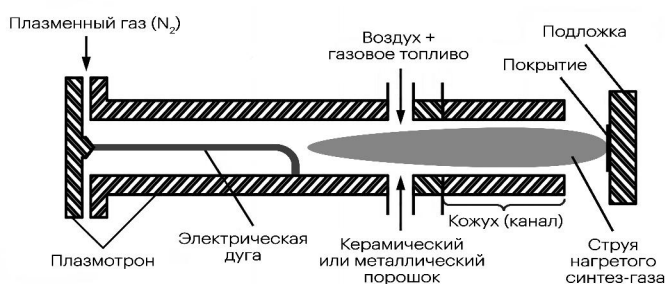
Схема разрабатываемой плазменно-топливной системы (ПТС) с плазменной струей и вводом углеводородов и с подачей порошков для нанесения покрытия на металлические детали
